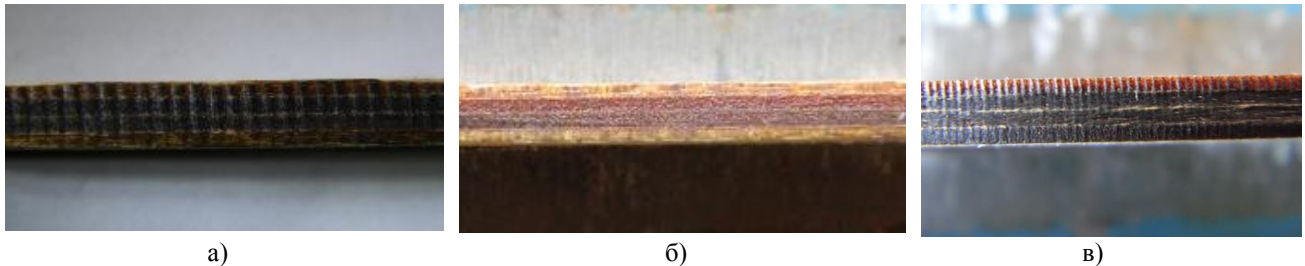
Вид реза образцов после лазерной резки: а) образец 1; б) образец 2; в) образец 3.
